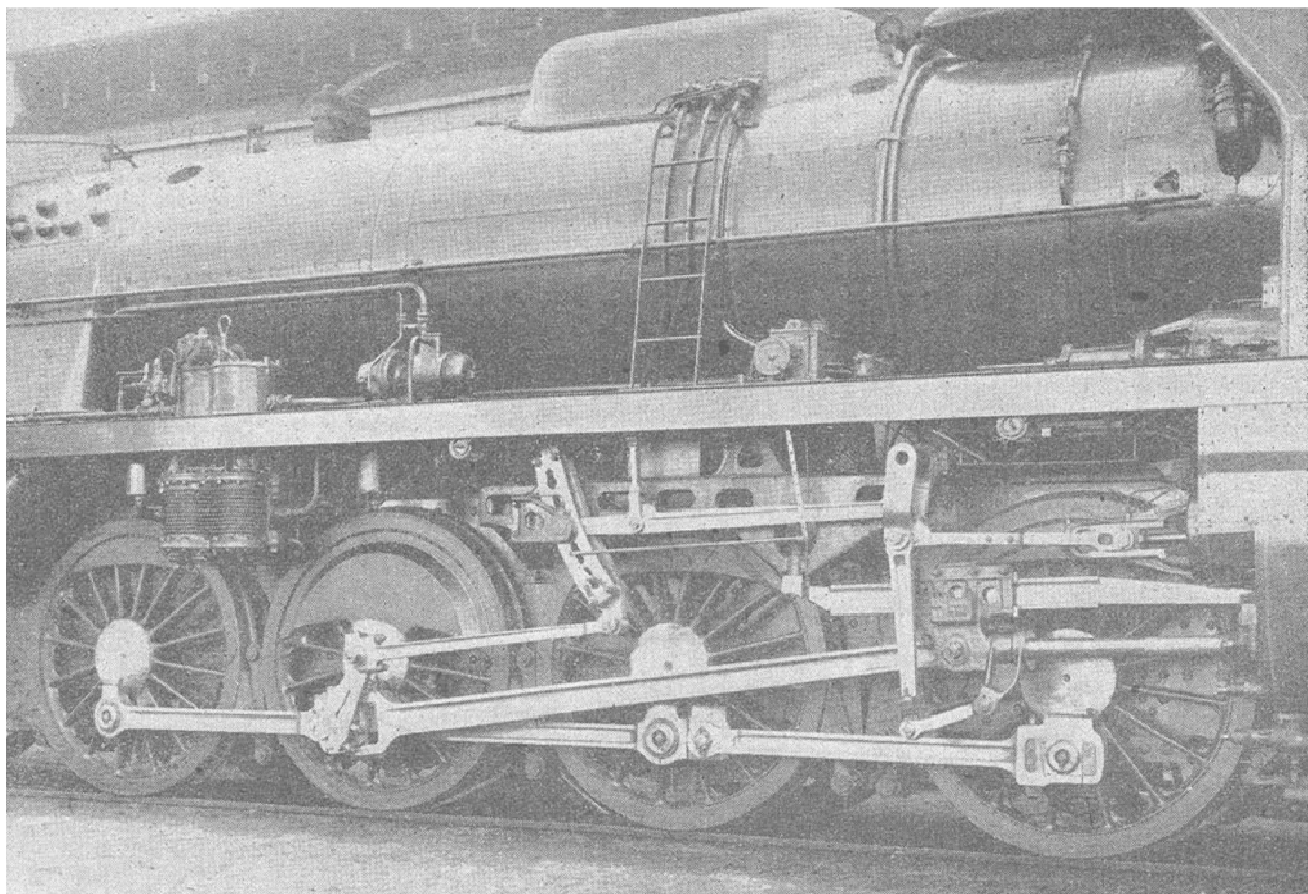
Conjunto de las ruedas motrices de la locomotora 141 P.
